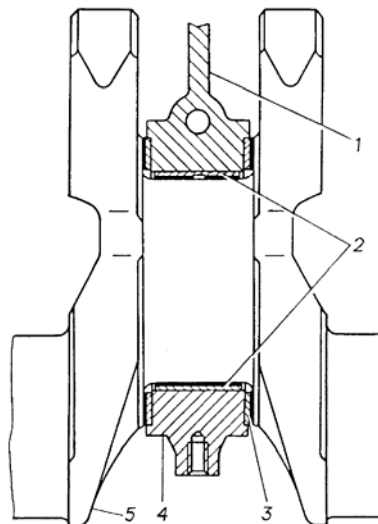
Средний (упорный) подшипник коленчатого вала:
